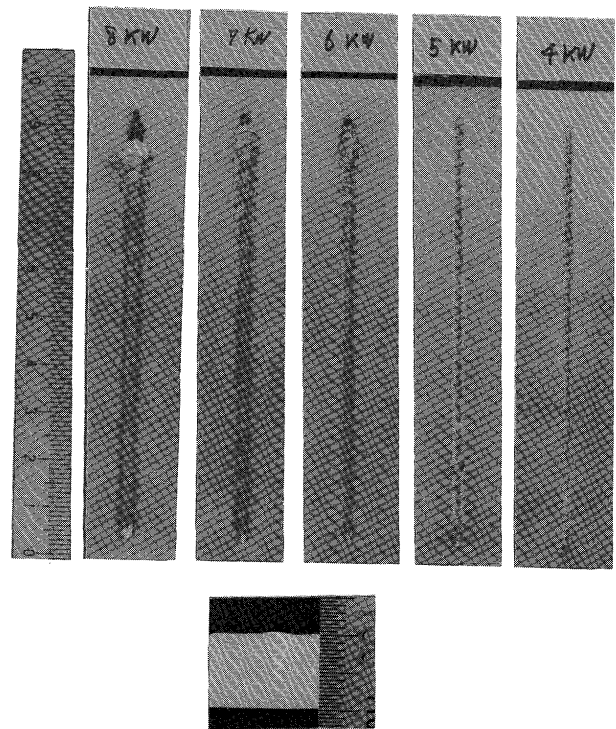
Schweissraupen-Erscheinung und ihr Querschnitt
